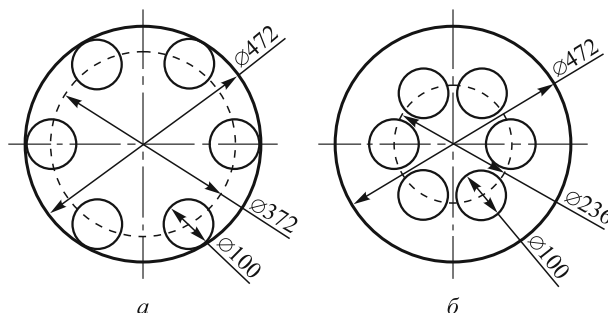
Схема вырезки исследовательских образцов из колесной заготовки:
